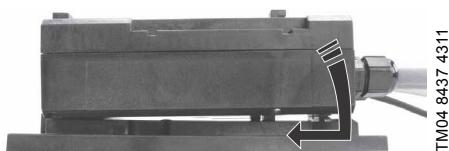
Montaje del cuadro de comunicación E-Box en la placa de montaje
